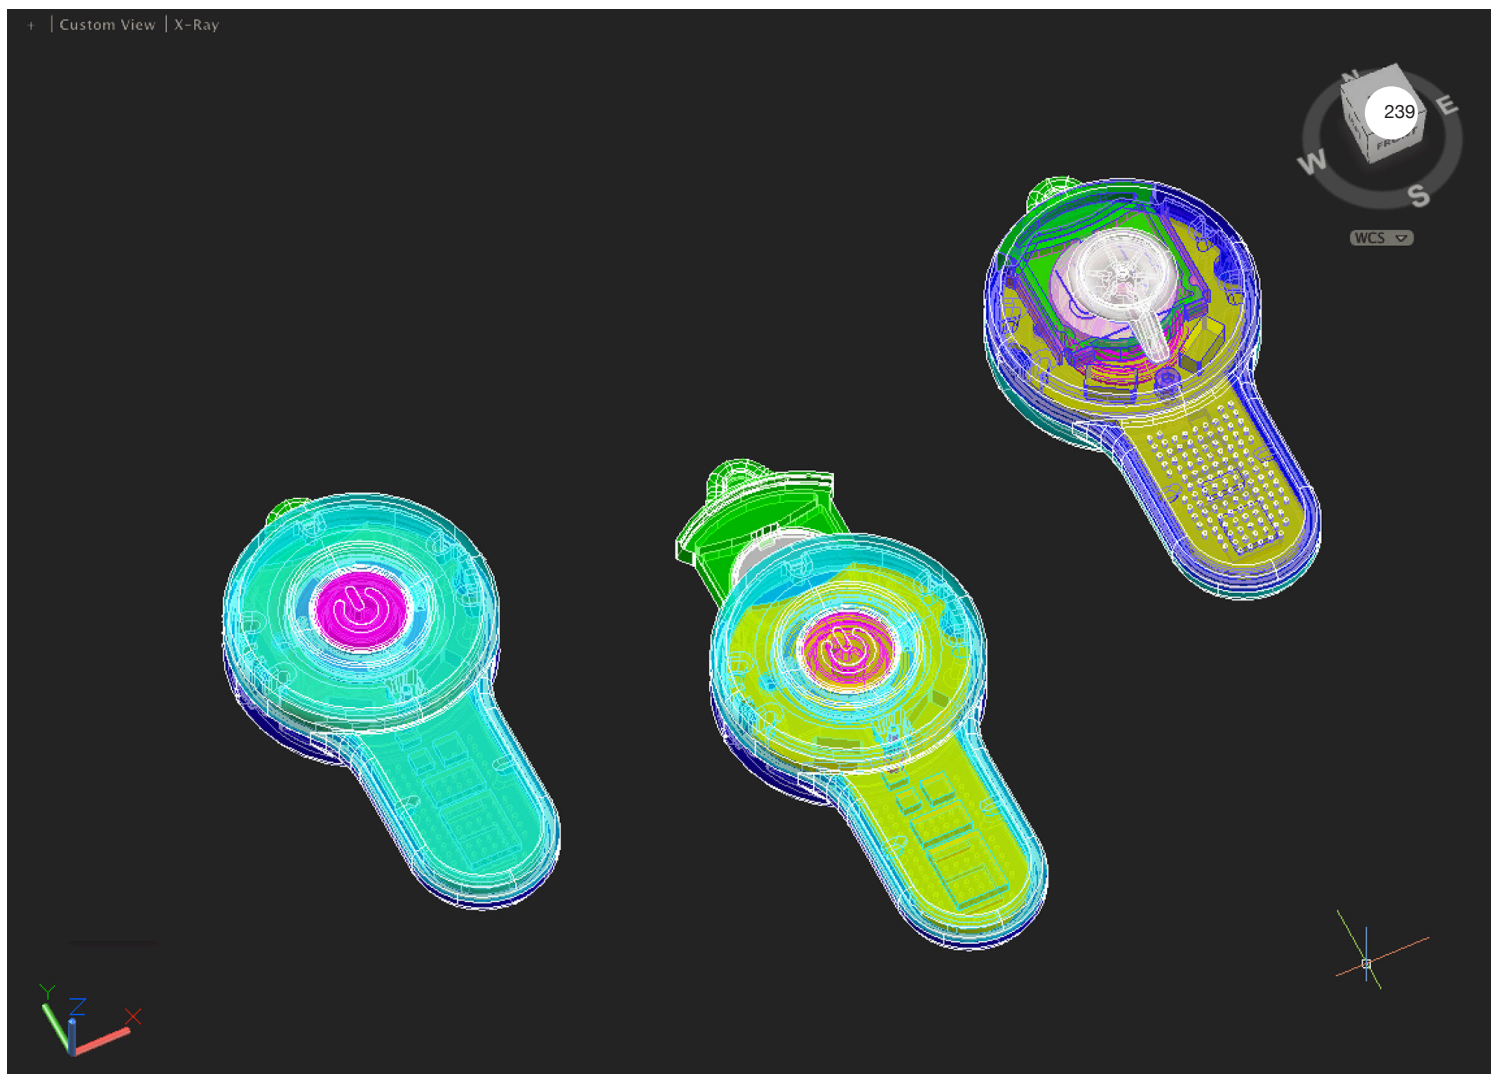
Modelos CAD 3D do sensor com todas as peças montadas.
